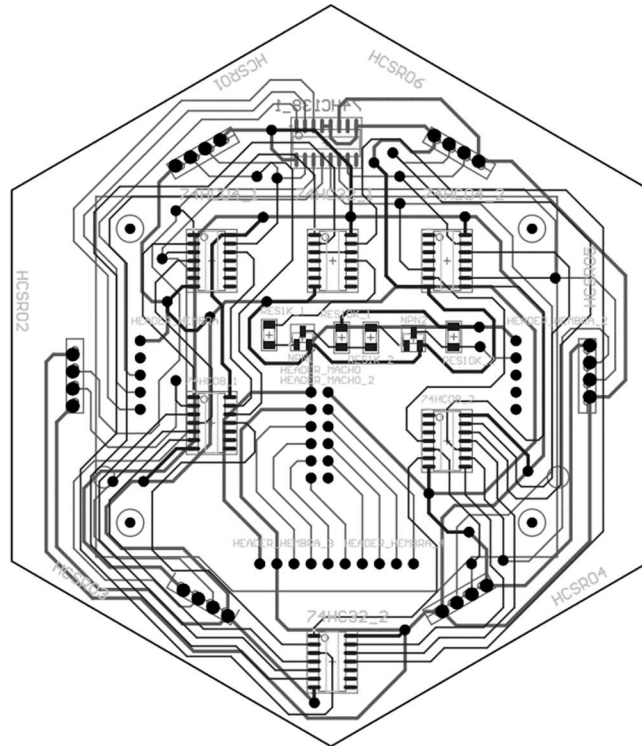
Vista 3D del PCB de la falda de sensores ultrasónicos.
